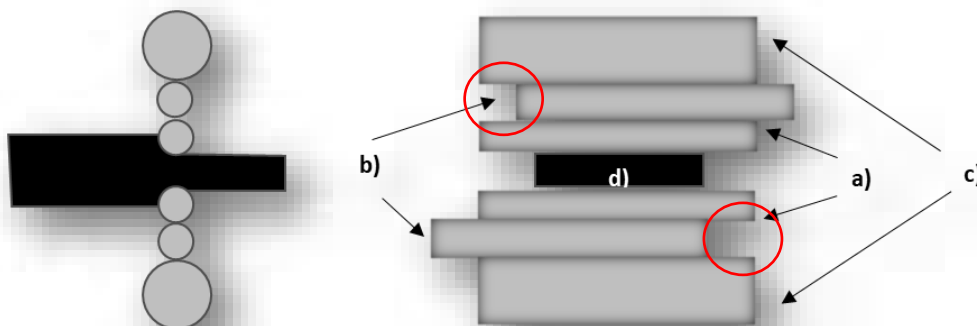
a) Rodillos de trabajo superior e inferior b) rodillos intermedios c) rodillos de apoyo d) lámina. Lado izquierdo es lado operador, lado derecho es lado motriz
